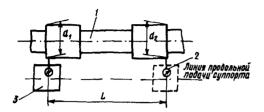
Схема для проверки правильности установки приспособления для проточки контактных колец:
